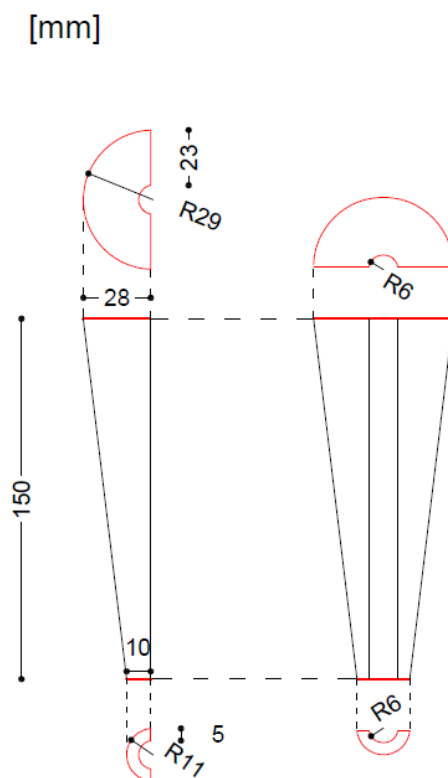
Cunhas metálicas dimensionadas para sistema porticado
